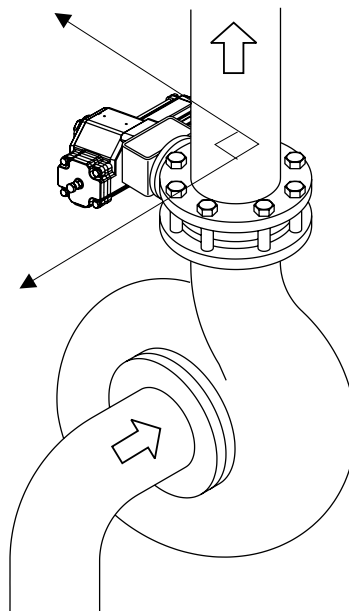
Installation d'une vanne papillon au refoulement d'une pompe centrifuge.
